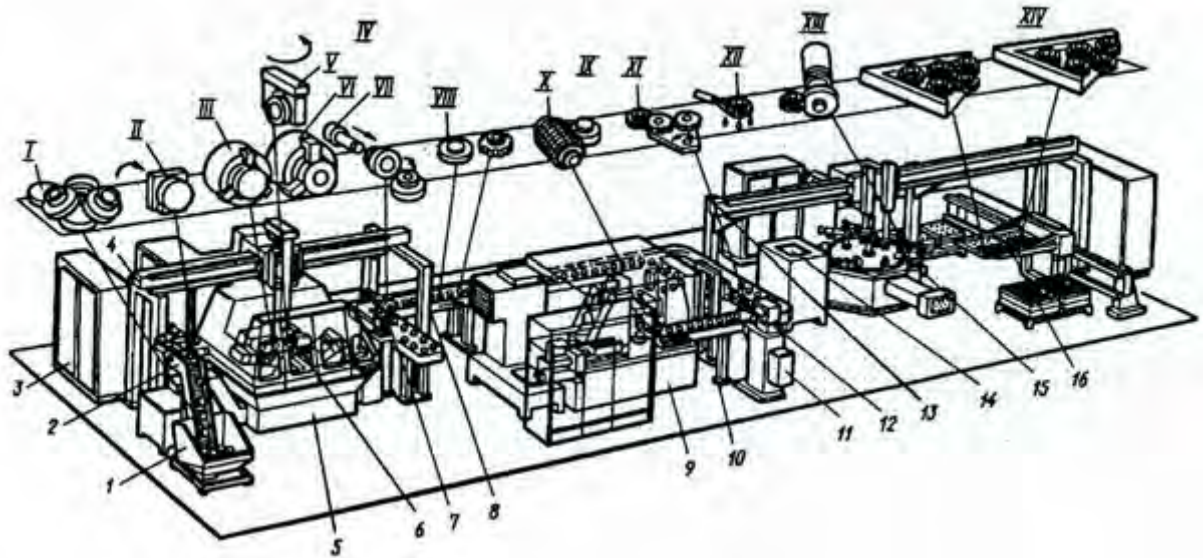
ГАЛ для оброблення зубчастих коліс
